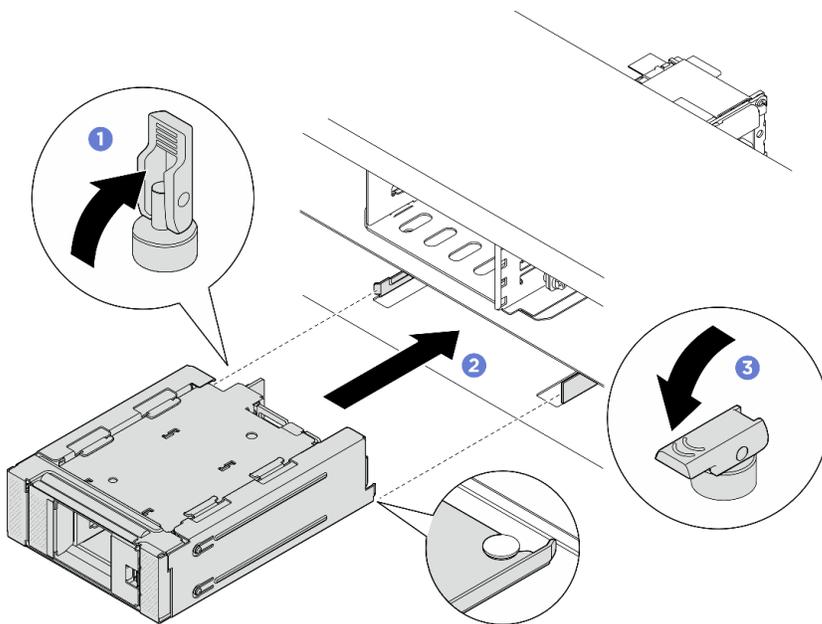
Установка переднего отсека для дисков M.2 с корпусом
